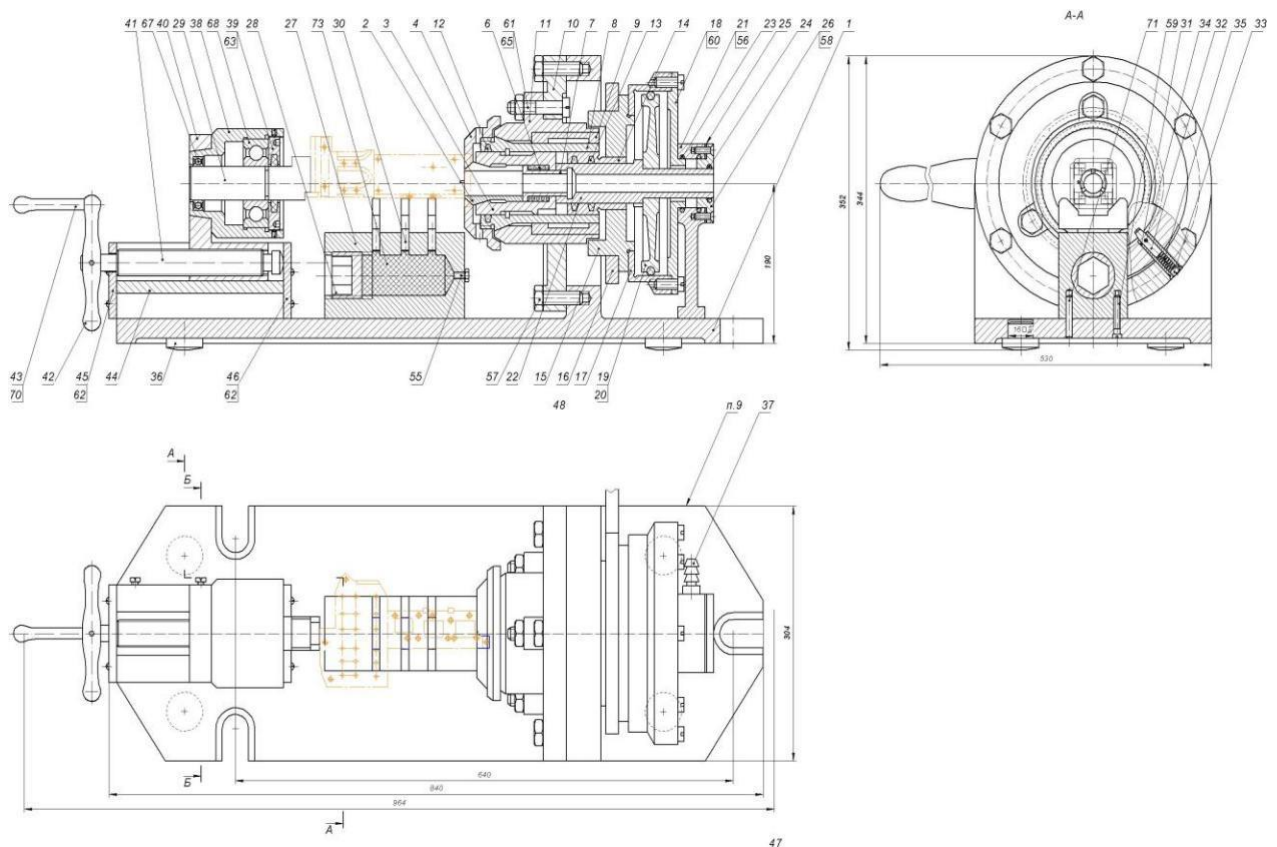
Ескіз пристрою для фрезерної операції з ЧПК
